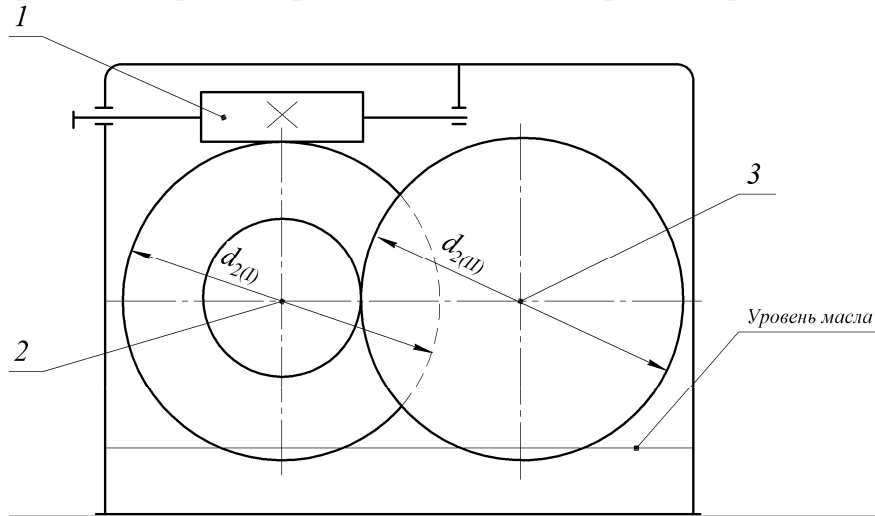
Редуктор ЧЦ с верхним расположением червяка
